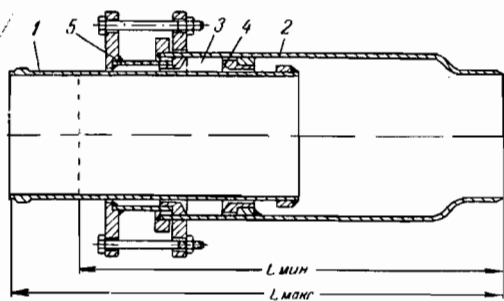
Одинарный сальниковый компенсатор сварной конструкции.
